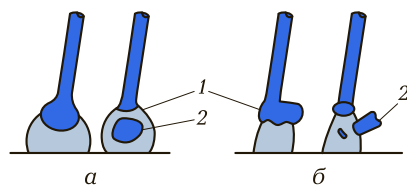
Крупнокапельный перенос металла при сварке:
